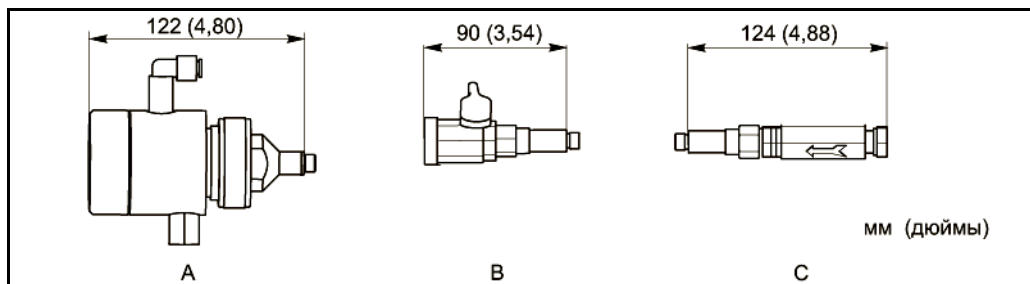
Защитные уплотнители входа/выхода промывочной камеры
